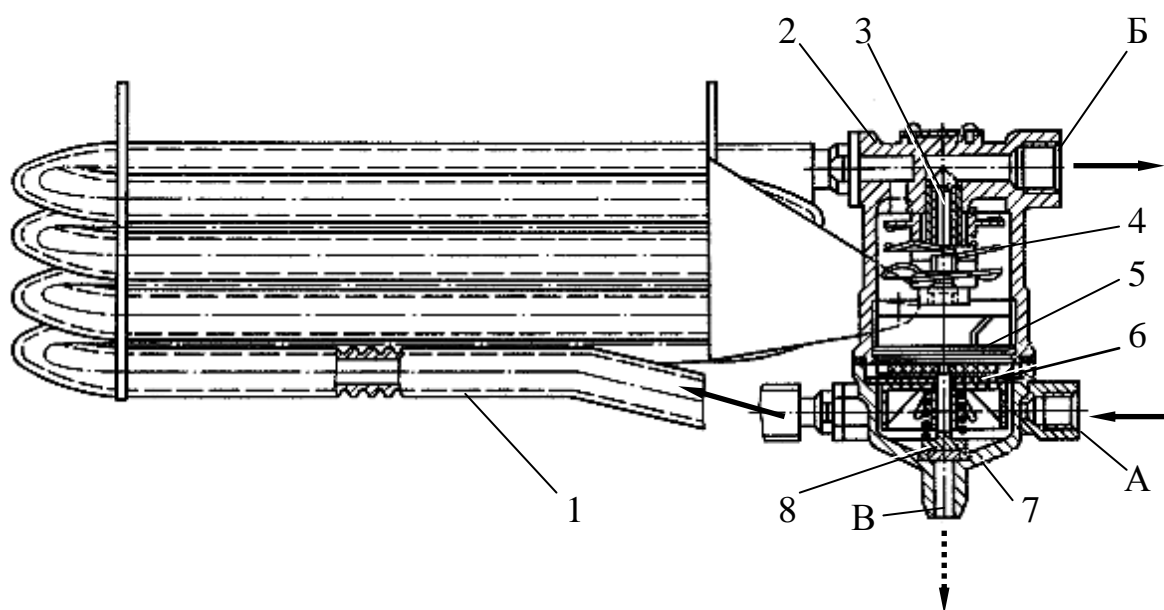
Водоотделитель питающей части тормозного привода грузового автомобиля-тягача КАМАЗ: 1 – радиатор с ребристыми трубками; 2 – корпус; 3 – пустотелый винт; 4 – направляющий аппарат; 5 – фильтр; 6 – мембрана; 7 – крышка; 8 – клапан слива конденсата; А – ввод от компрессора; Б – вывод к регулятору давления; В – атмосферный вывод
